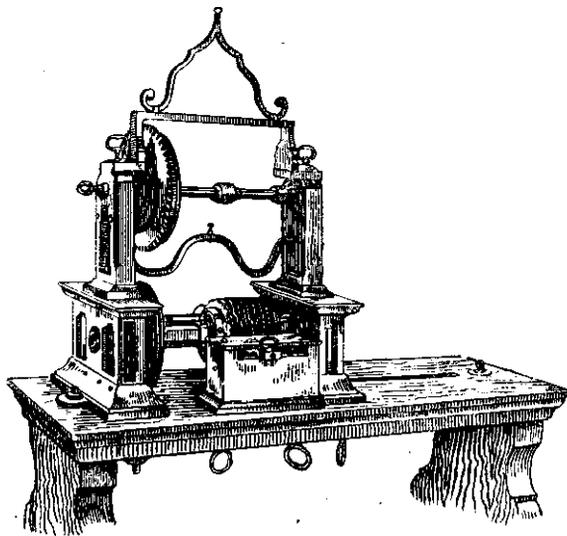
Гильоширный токарно-овальерный станок Партова 1718 г. (общий вид).
